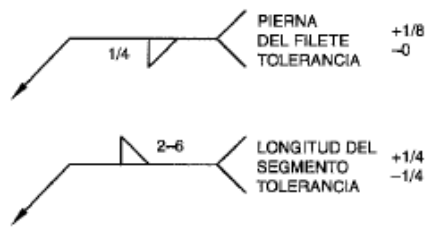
Tolerancias de las Dimensiones de Soldadura. [15]
